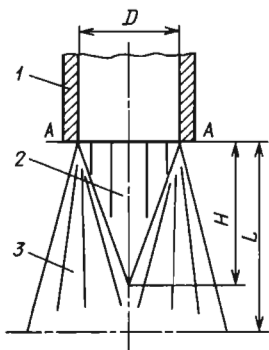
Схема газового потока при местной защите зоны сварки
